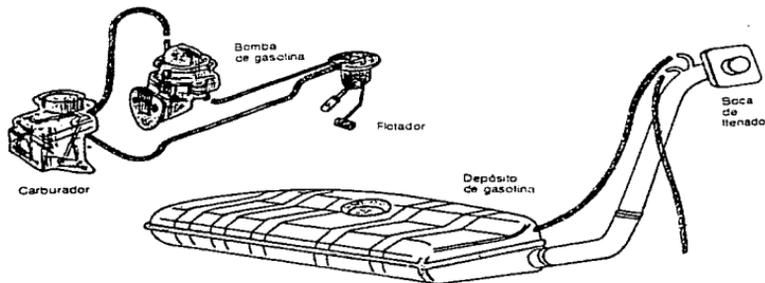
a Lugar del montaje del sensor de nivel de combustible (flotador)
